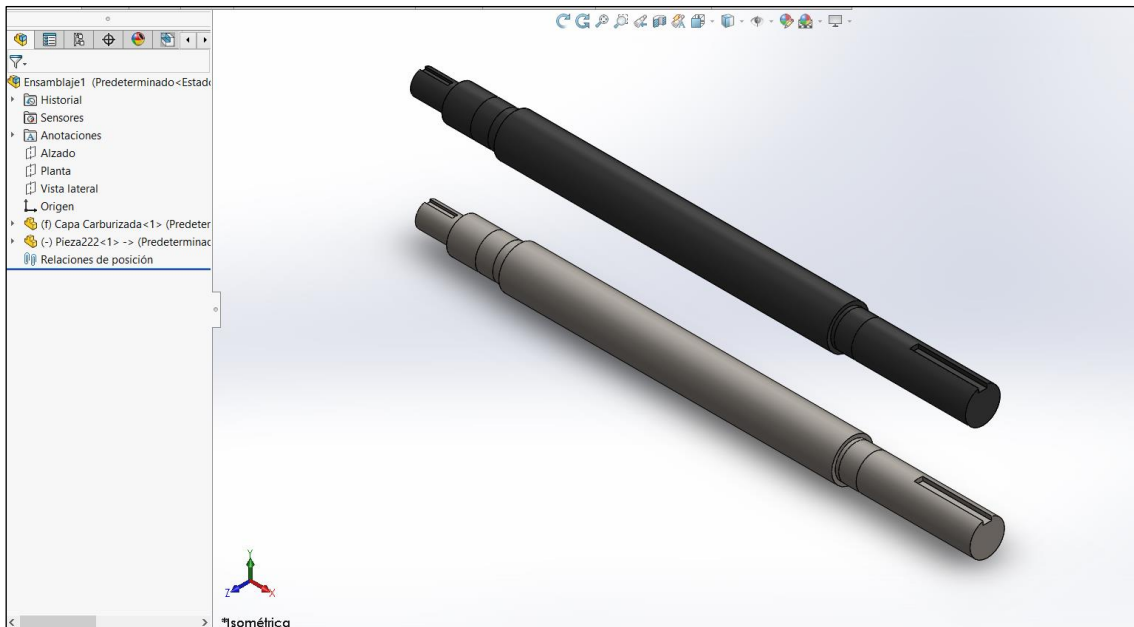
Muestra de la capa carburizada y el eje principal en 3D.
